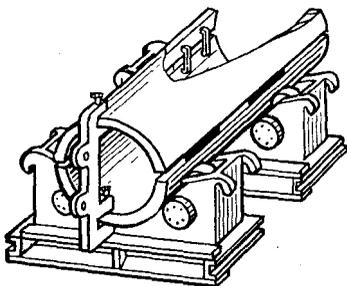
Сборка обечайки с двумя продольными стыками
